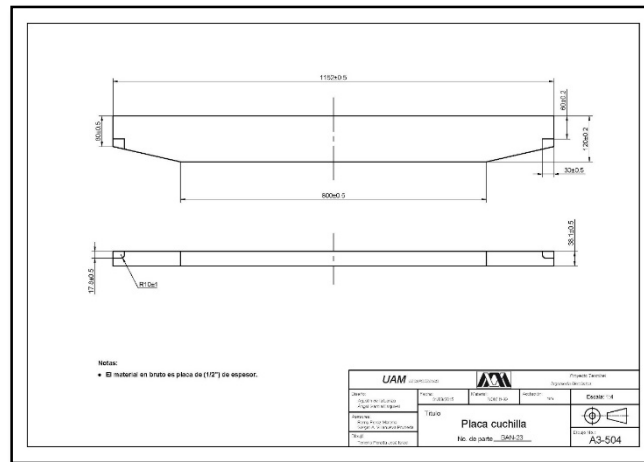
Plano A3-504 Placa cizalla generado en AutoCAD.
